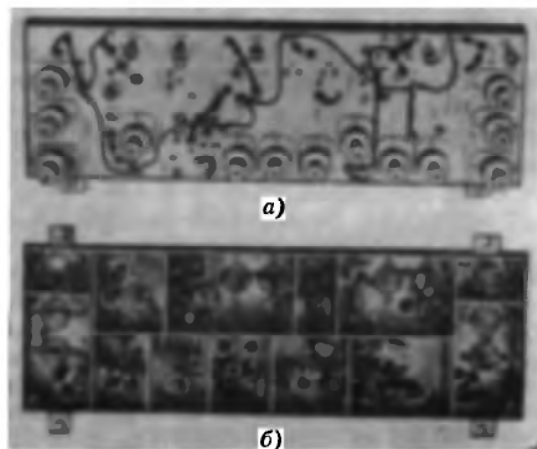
Коробчатое паяное шасси: а) вид снизу; б) вид сверху
